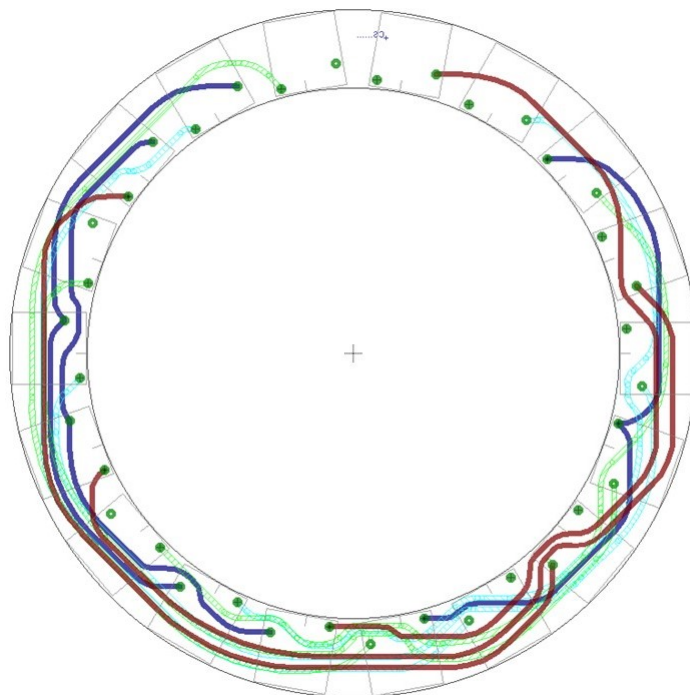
Disegno del Circuito Stampato per il Motore di Brandeggio
